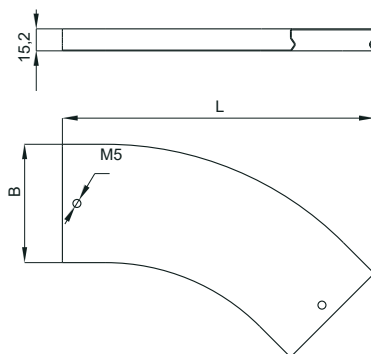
Крышка поворота плавного на 45° /
